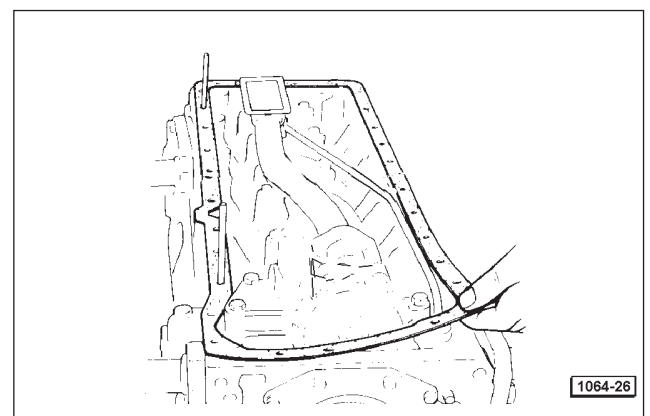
Die Dichtung der Motorölwanne anbringen.
